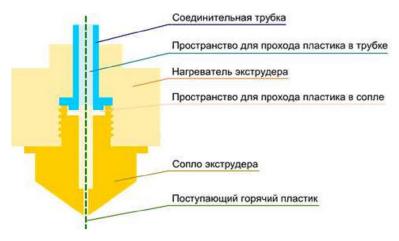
Схема расположения сопла и соединительной трубки в нагревательном блоке экструдера
